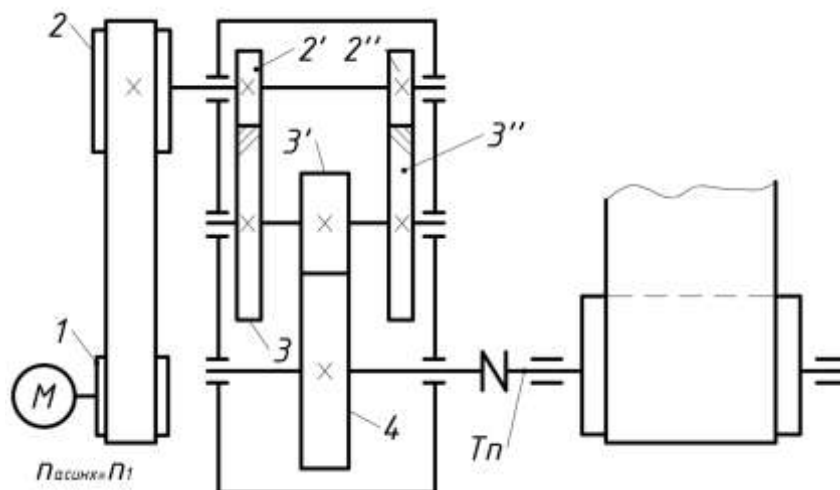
Кинематическая схема привода (ременная передача и двухступенчатый цилиндрический редуктор с раздвоенной быстроходной ступенью):
